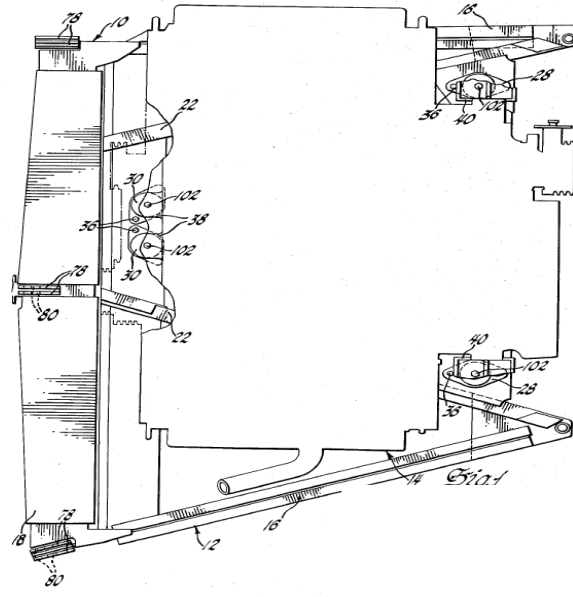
Güç paketinin motor beşiği yardımıyla şasiye montajı
